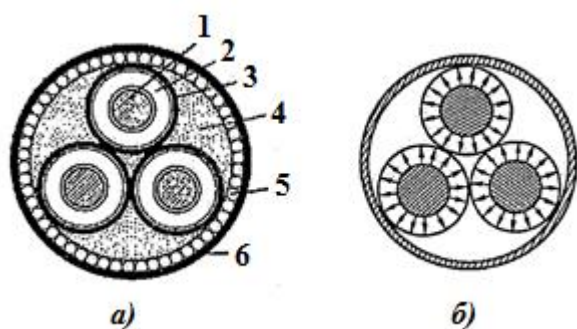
Конструкция кабеля на напряжение 20...35 кВ: 1 – токопроводящая жила; 2 – бумажная фазная изоляция; 3 – фазная свинцовая оболочка; 4 – кабельная пряжа; 5 – стальная проволочная броня; 6 – наружный защитный покров
